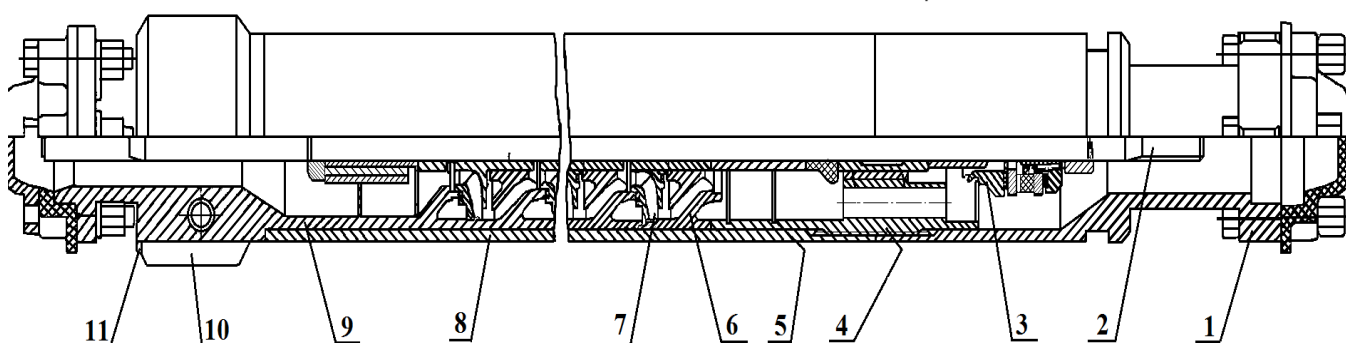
Модуль-секция насоса: 1 – головка; 2 – вал; 3 – опора; 4 – верхний подшипник; 5 – кольцо; 6 – направляющий аппарат; 7 – рабочее колесо; 8 – корпус; 9 – нижний подшипник; 10 – ребро; 11 – основание.
